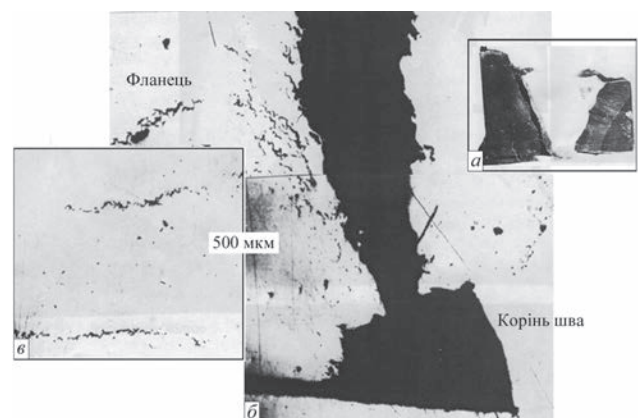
Область руйнування зварного шва приварювання фланця до труби: а – макроструктура; б – магістральна тріщина; в – зигзагоподібні ланцюжки в металі фланця зі сталі 20
